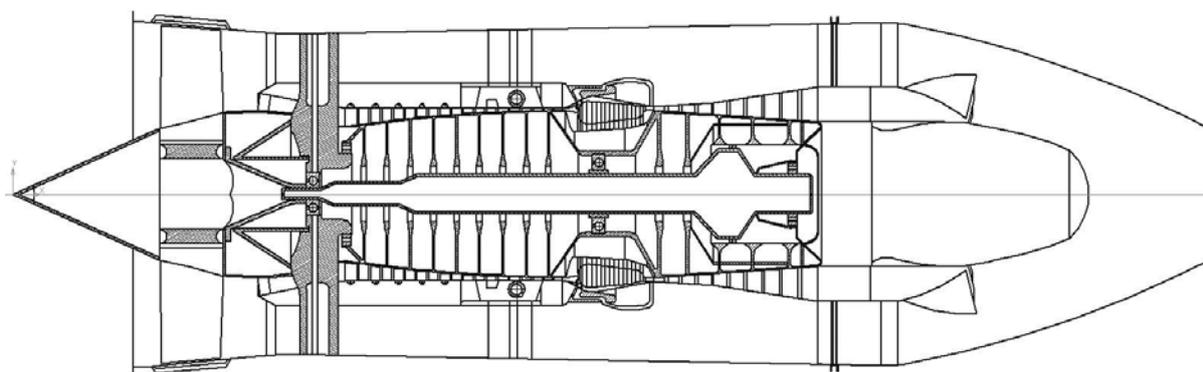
Конструктивно-компоновочная схема двигателя для высотного БЛА
